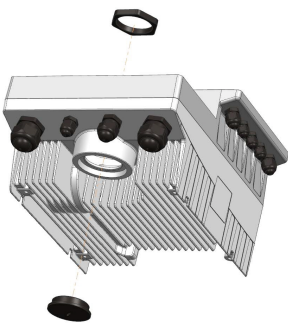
Gehäuse des Kondensatormoduls auf die Motoradapterplatte aufsetzen
